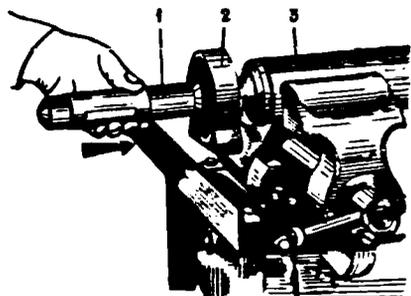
Установка упругой опоры на передний карданный вал: 1 - оправка А.74035; 2 - упругая опора; 3 - задняя часть переднего карданного вала
